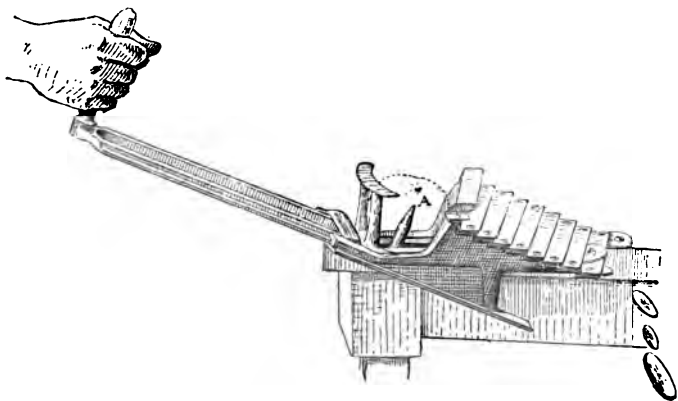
Machine à couper et trancher, « la Simplex ».
